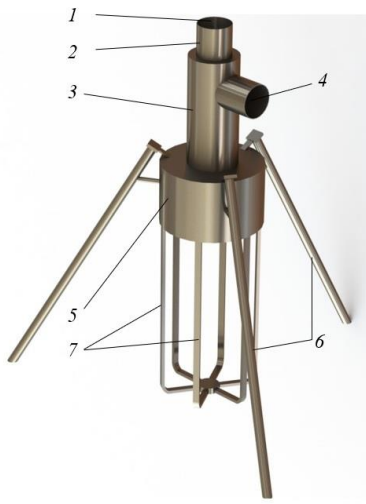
Цифровой двойник классификатора с соосно расположенными трубами: 1 – входной патрубок, 2 – внутренняя цилиндрическая труба, 3 – внешняя цилиндрическая труба, 4 – выходной патрубок, 5 – цилиндрическая часть, 6 – опоры, 7 – металлическая конструкция для съемной емкости
